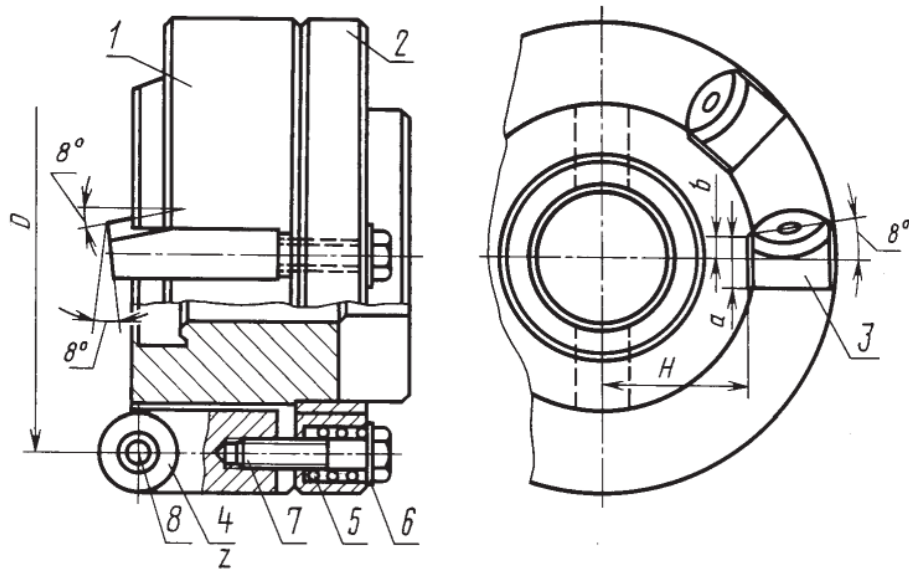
Фреза торцева з механічним кріпленням пластин ГОСТ 26595-
